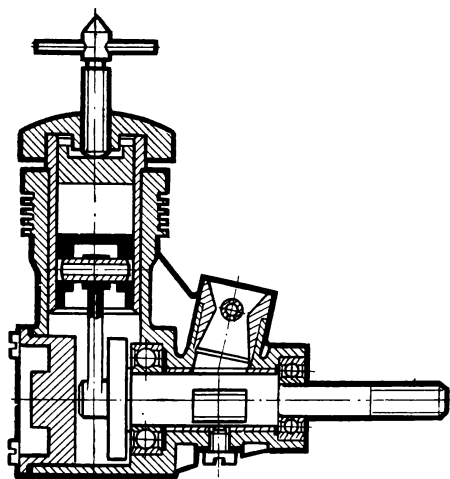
Конструкция двигателя МД2,5К «Метеор».
